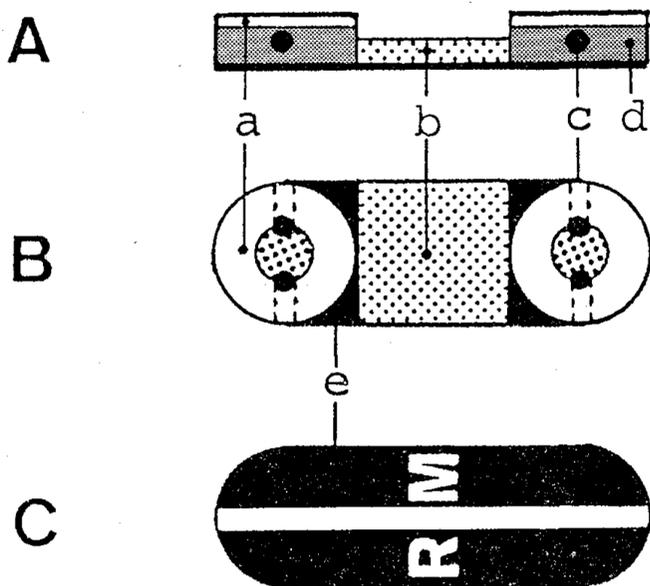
A 側面図 B 正面図 C 背面図 (実物大)
